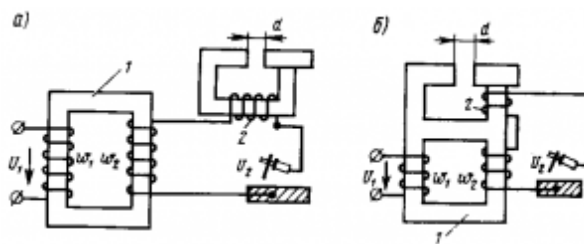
Принципиальные схемы сварочных трансформаторов: а —с внешней индуктивностью (реактором), б – с реактором на общем сердечнике; 1 — трансформатор; 2 — реактор
